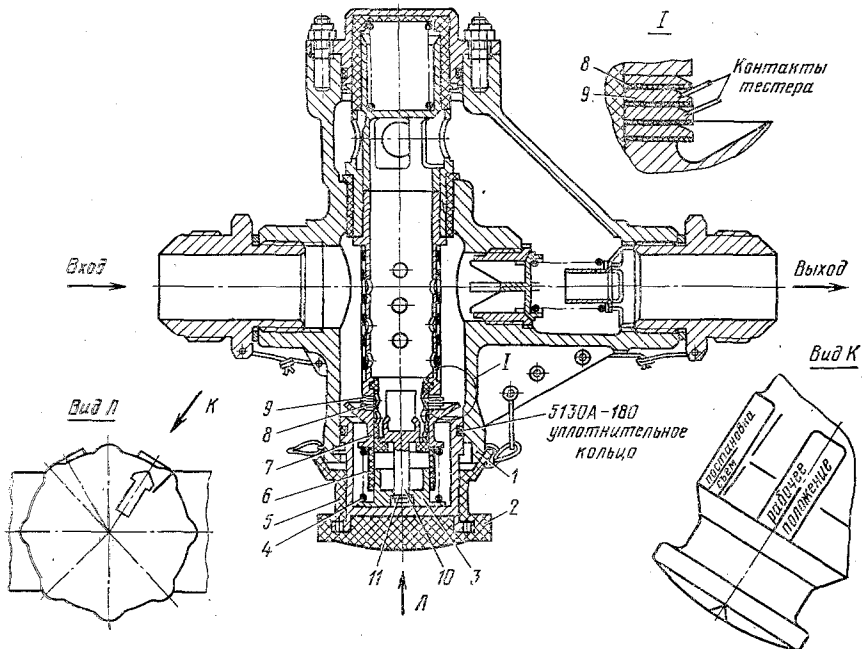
Фильтр-сигнализатор ФСС-1 редуктора ВР-8А:
